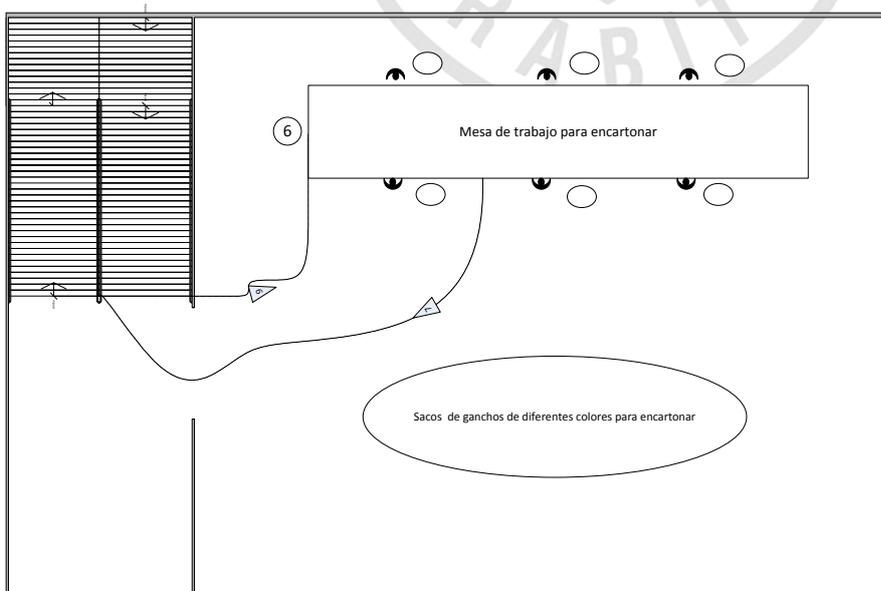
Plano: Vista de Planta del 3r piso LEÓN PLAST con la anterior distribución
